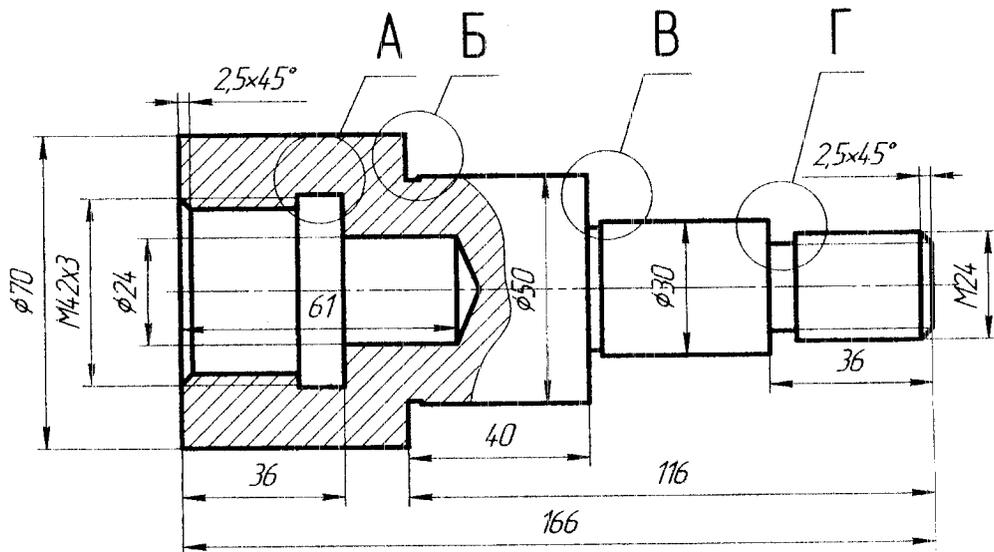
Вал з канавками під шліфування та різьбовими проточками
